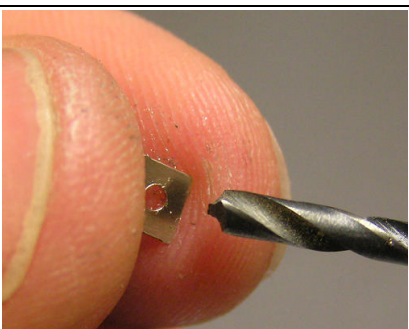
Das Loch beiseitig mit dem Bohrer entgraten.
